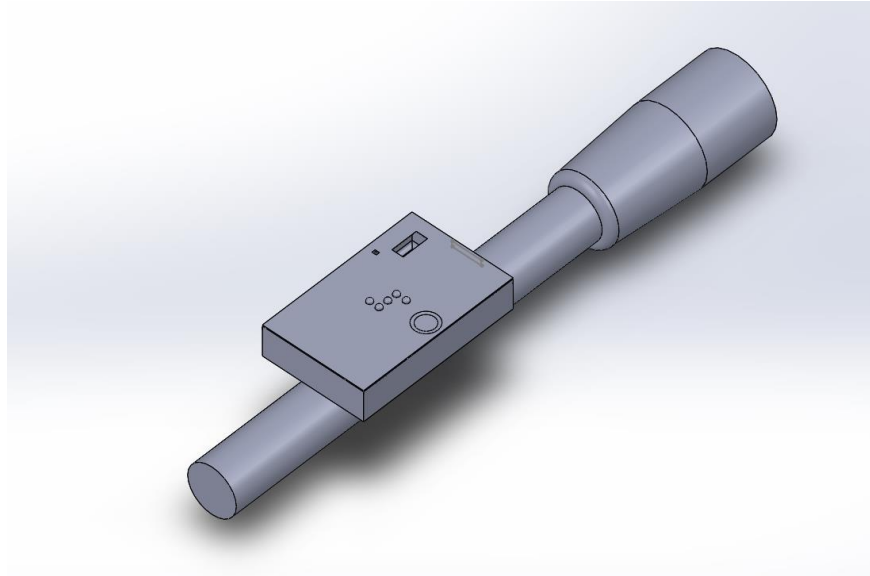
Carcasa Dispositivo 1 ensamblaje
